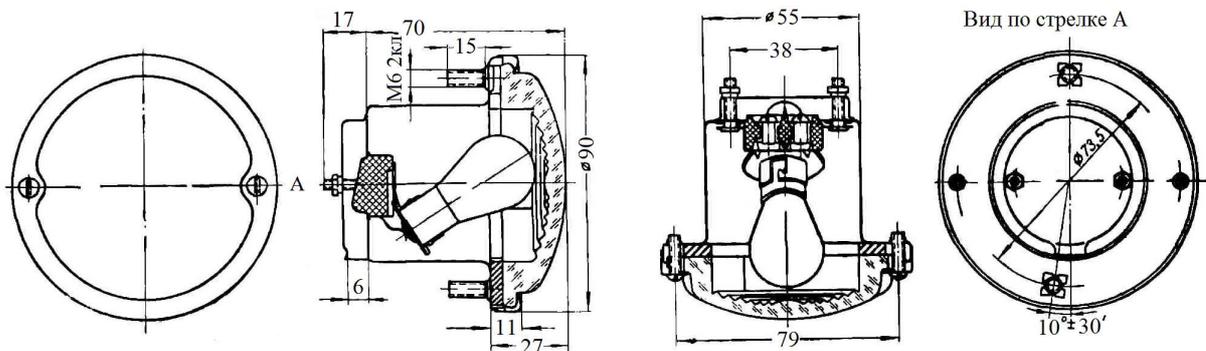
Подфарник ПФ-101, габаритные размеры
